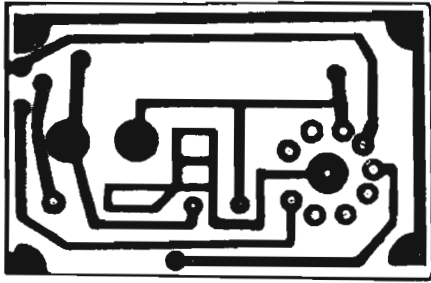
A - Il disegno originale riproduce, in tutti i suoi dettagli, il circuito stampato in dimensioni molto maggiori.
